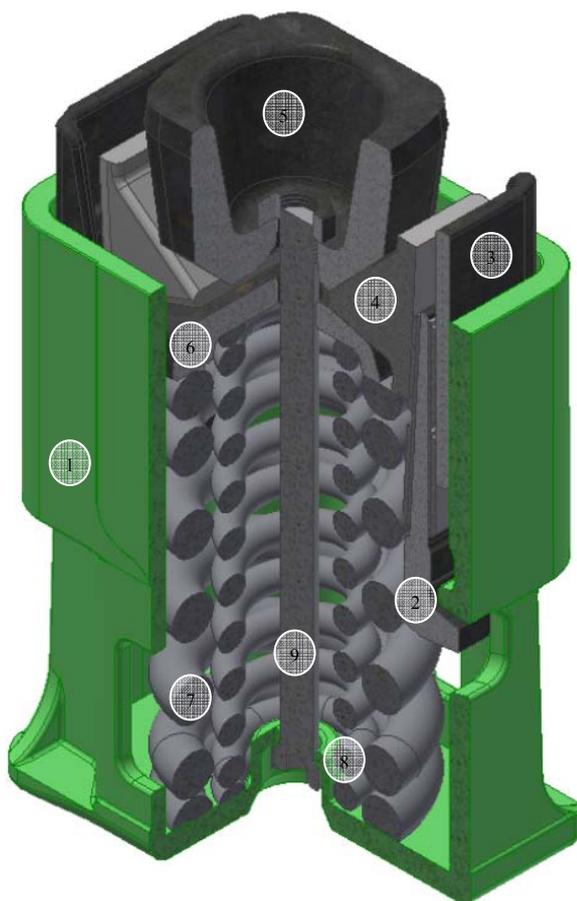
Поглощающий аппарат АПФК-110 класса Т1: 1-корпус, 2-пластина неподвижная, 3-пластина подвижная, 4-клин, 5-конус нажимной, 6-пластина опорная, 7,8-пружины, 9-болт стяжной с гайкой
